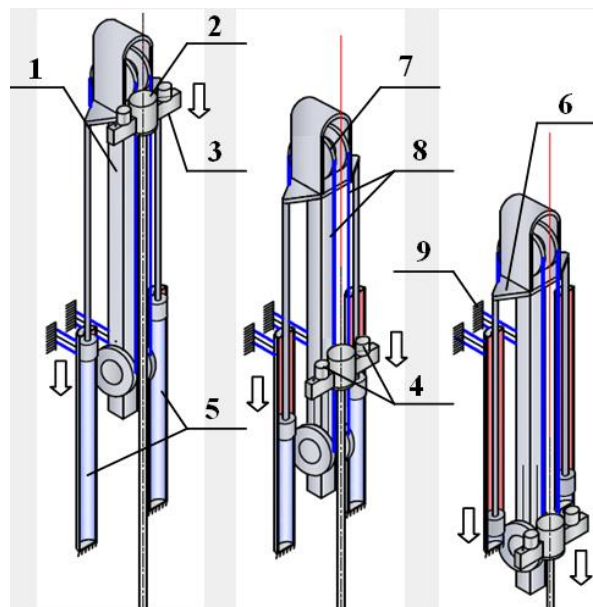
Система подачи канатно-поршневого типа бурового станка T130XD фирмы Schramm, INC. США.
